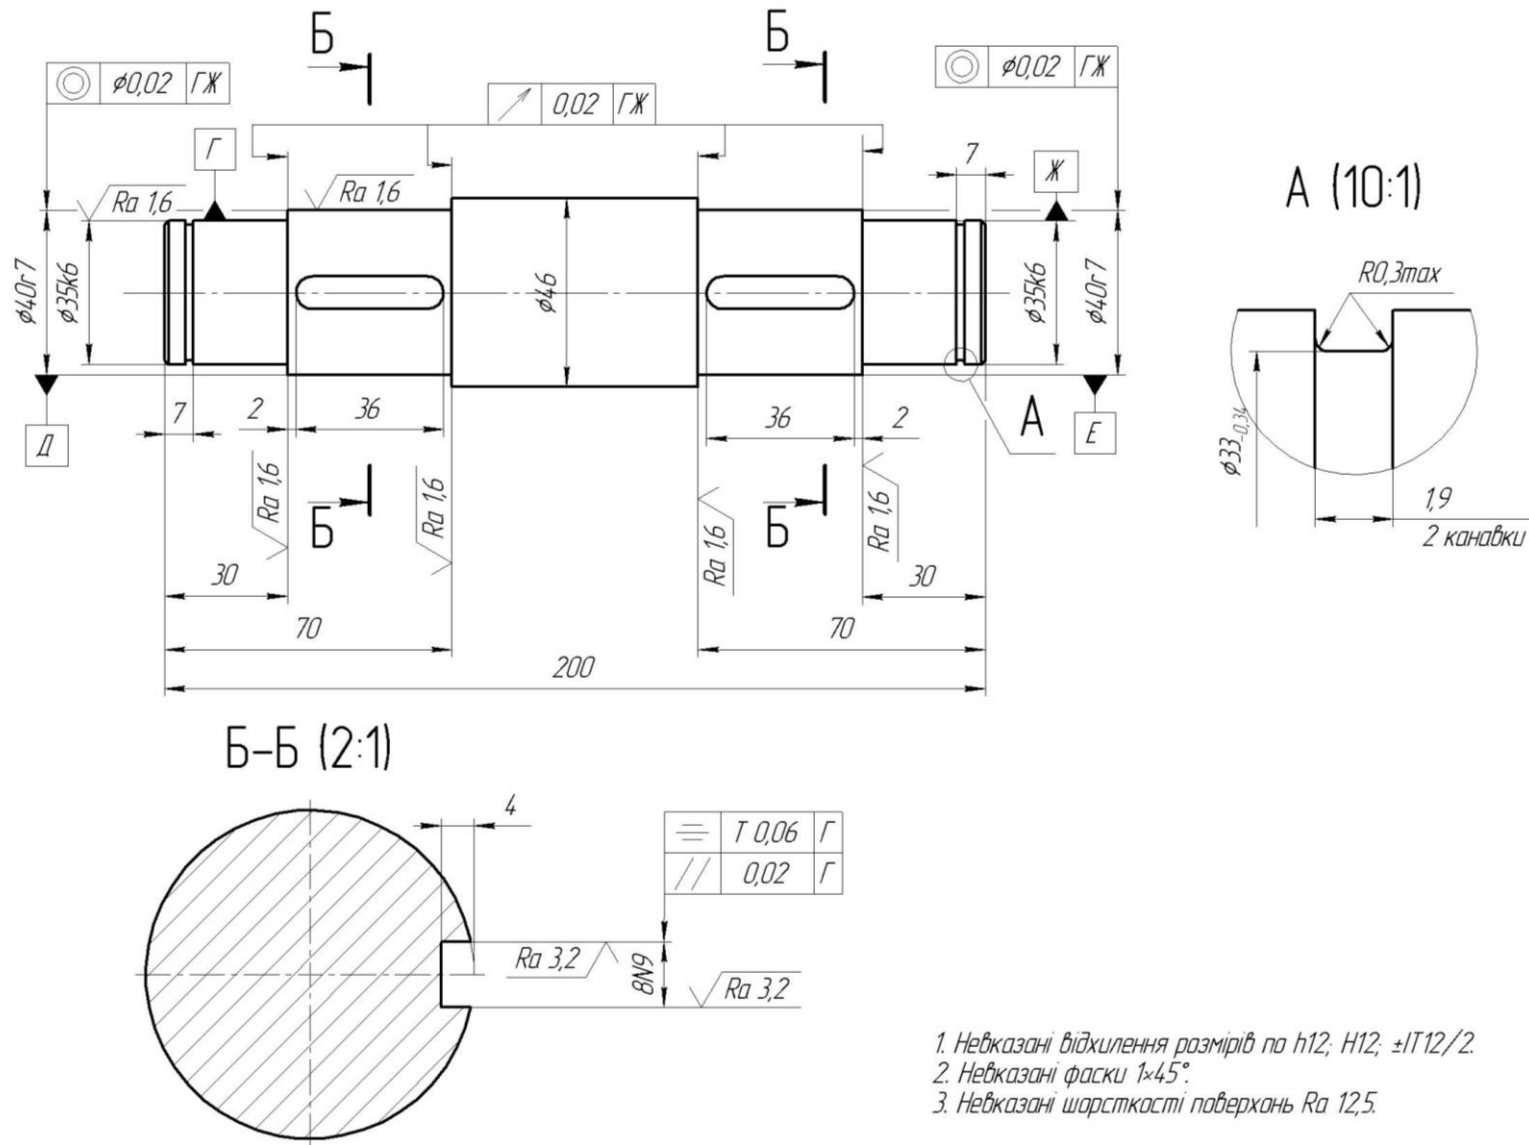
Кресленник деталі «Вал проміжний»
